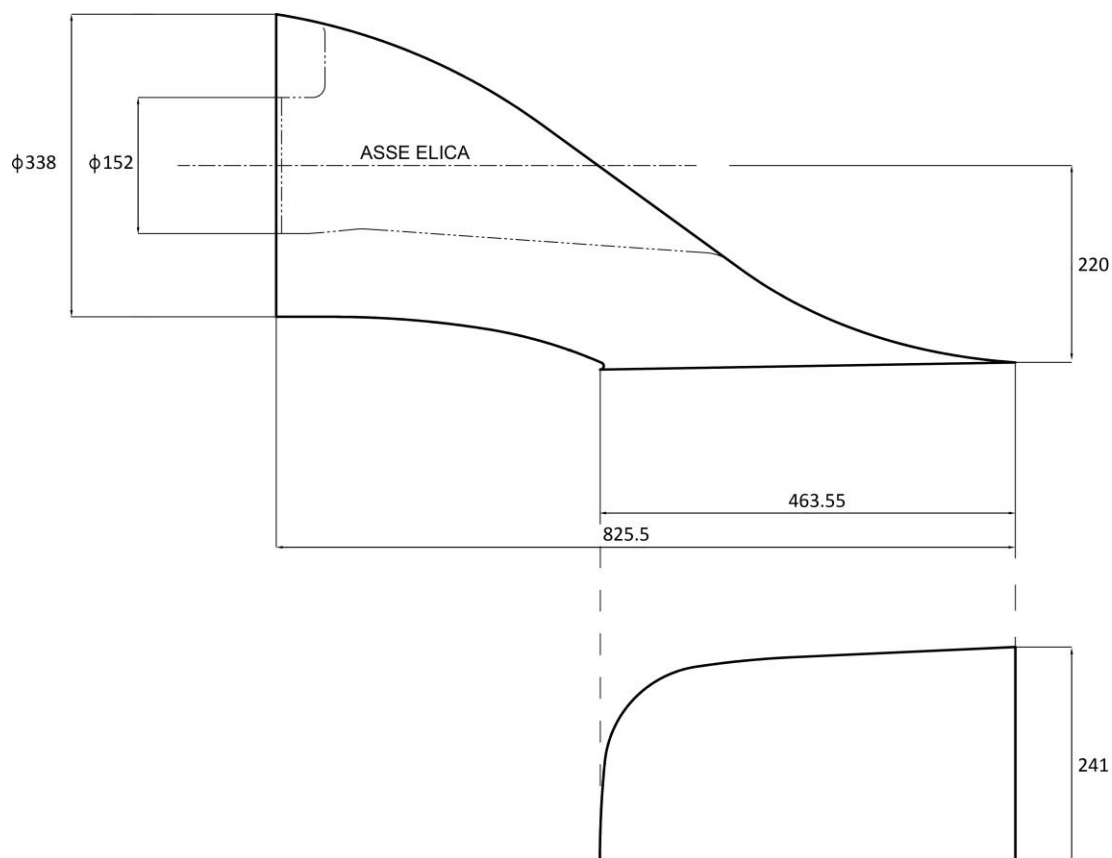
Vista in sezione meridiana del condotto e di (metà sezione d'imbocco). Le dimensioni dell'ingombro sono espresse in mm
